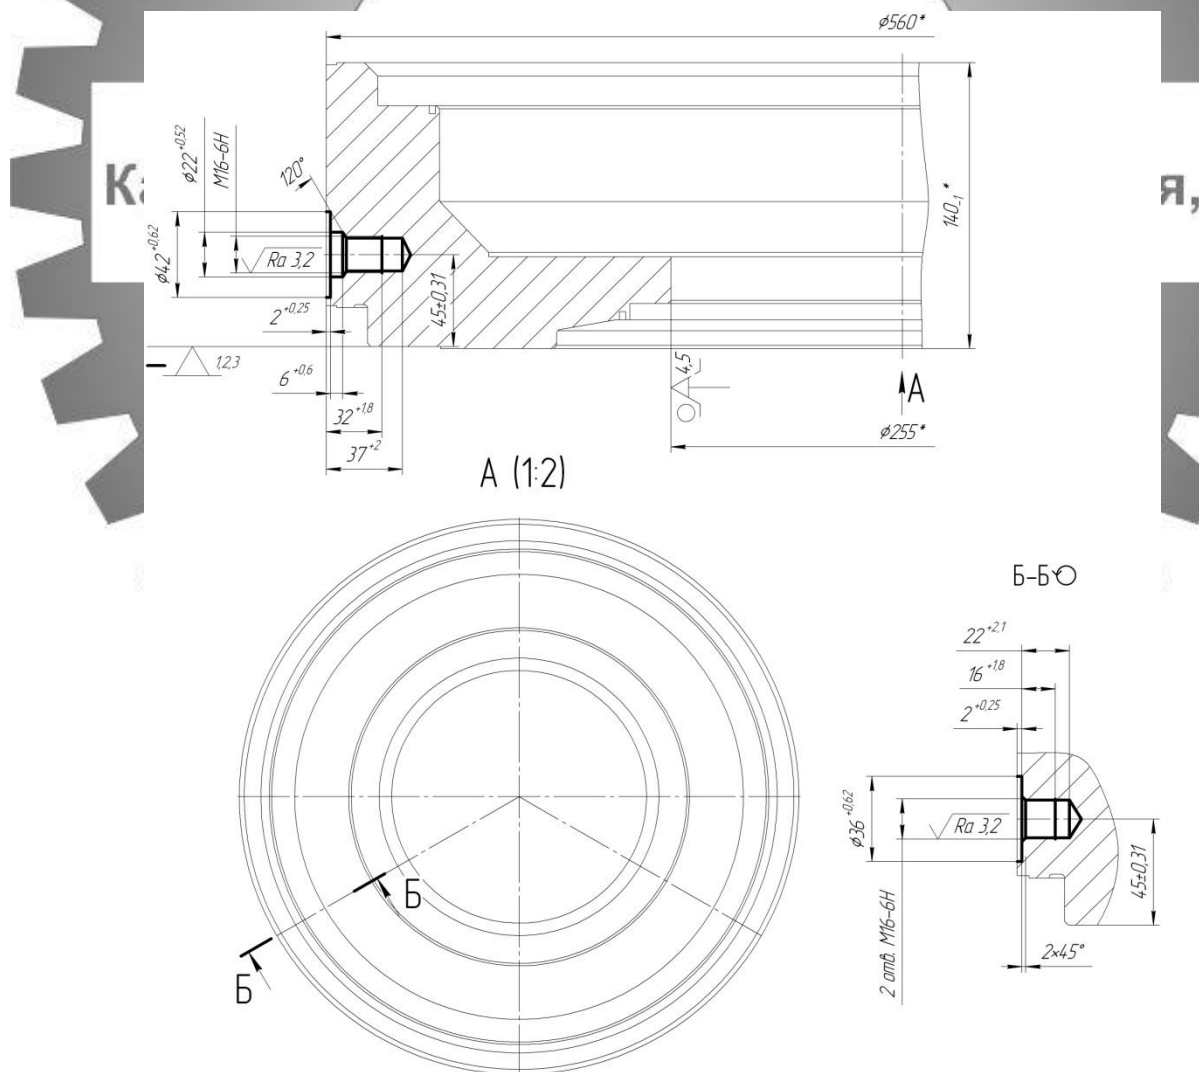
Схема базування заготовки на комплексній з ЧПК операції
